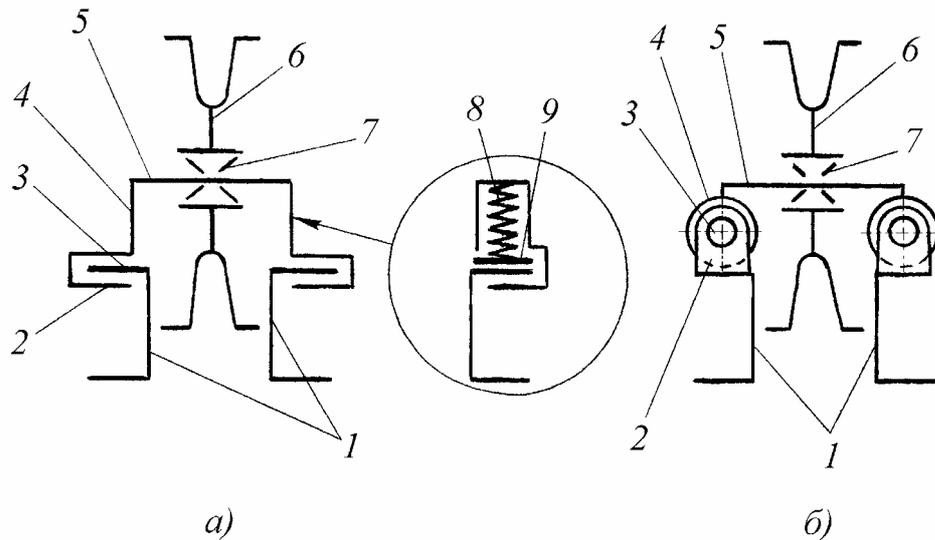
Схемы установки направляющего колеса на ползунах
